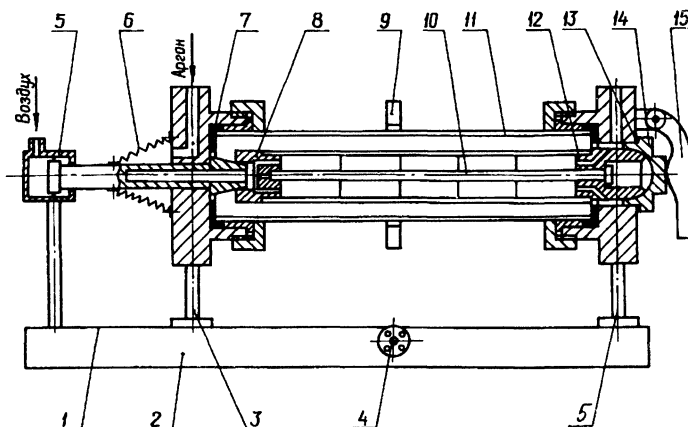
Установка для сварки изделий из порошковых материалов
